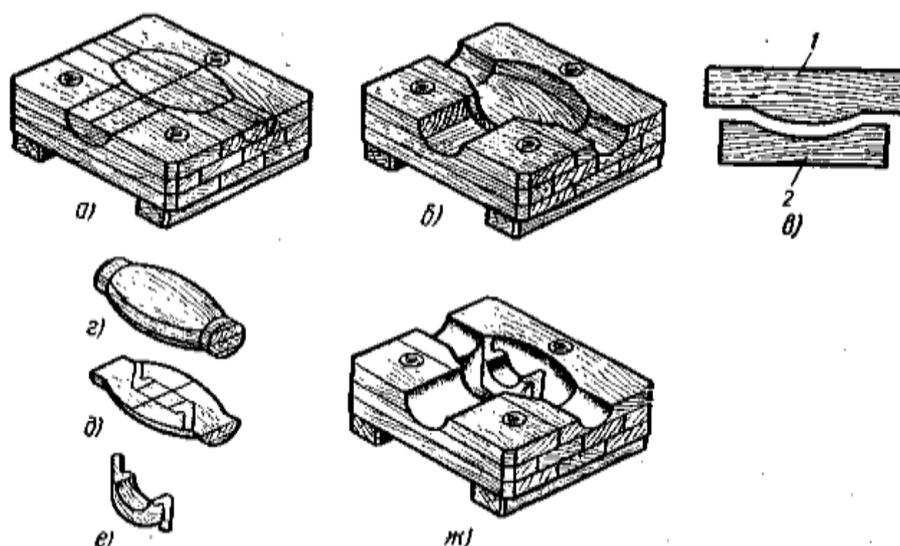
Последовательность изготовления стержневого ящика к модели корпуса вентиля.
